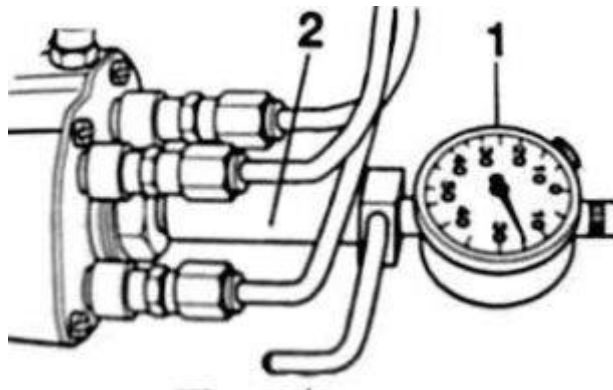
Індикатор ИЧ-10 в корпусі ПНВТ
